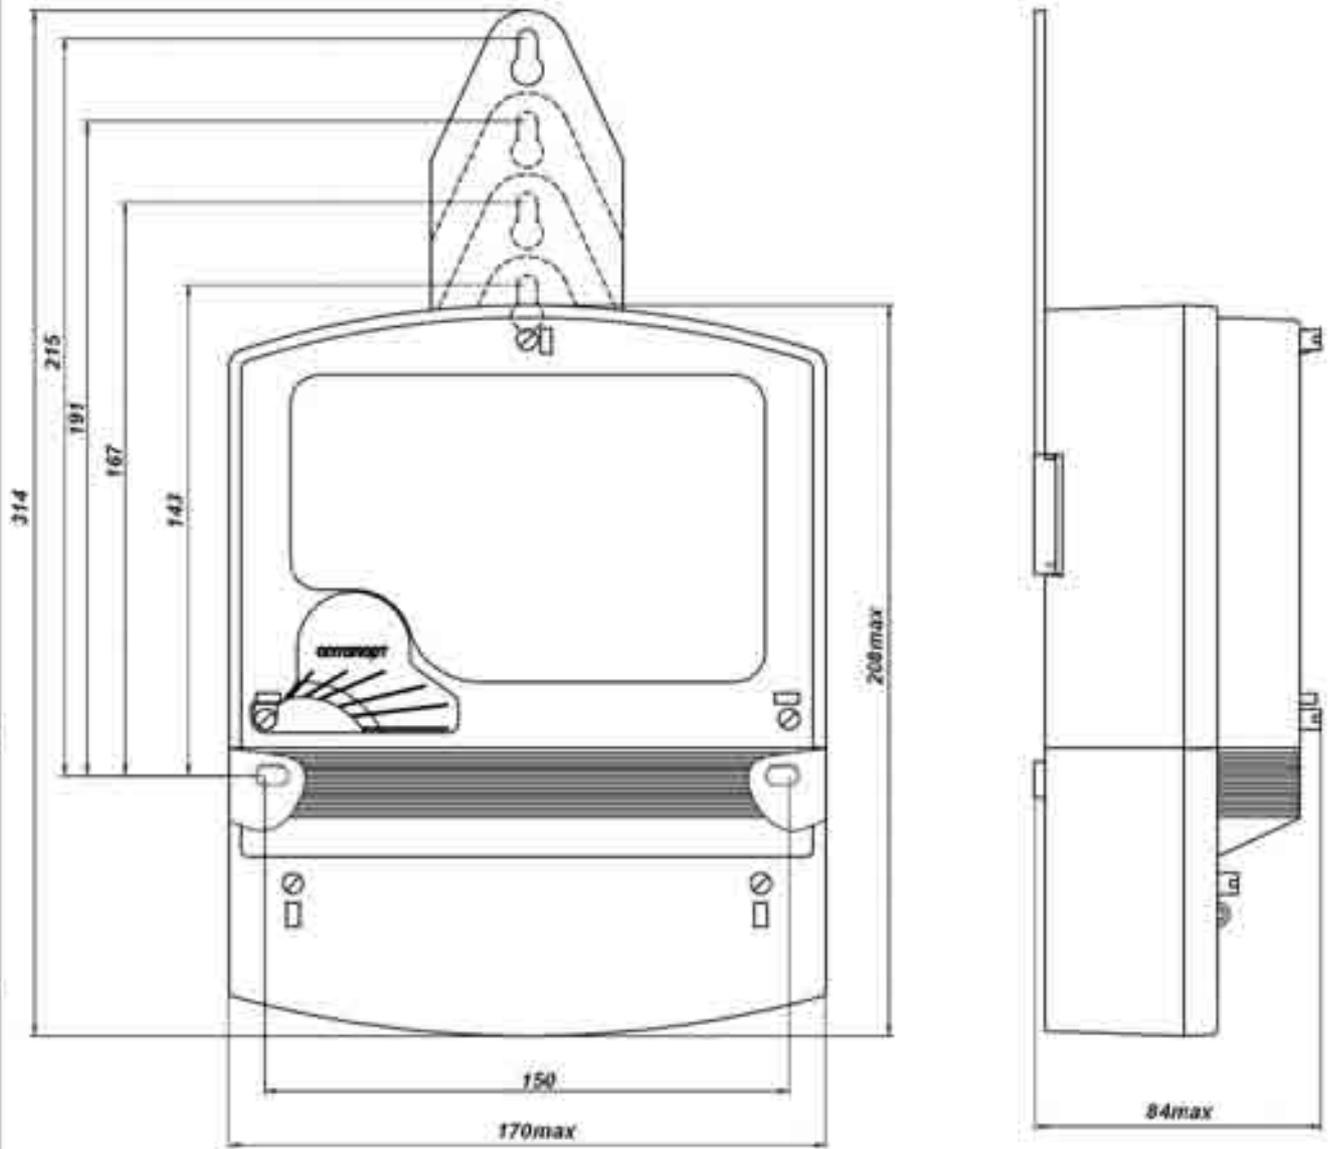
Габаритные и установочные размеры счетчиков НІК 2303...
